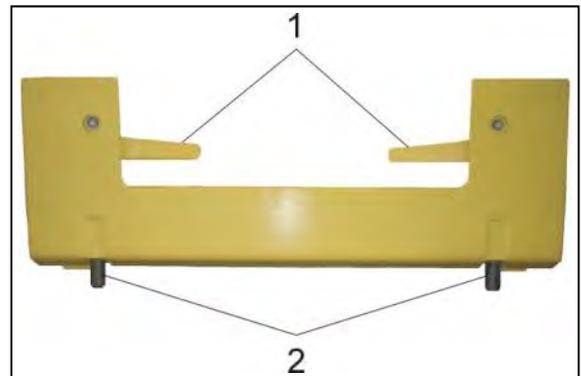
Крепление быстродействующего зажима 1- Рычаг, 2- Страховой штифт
